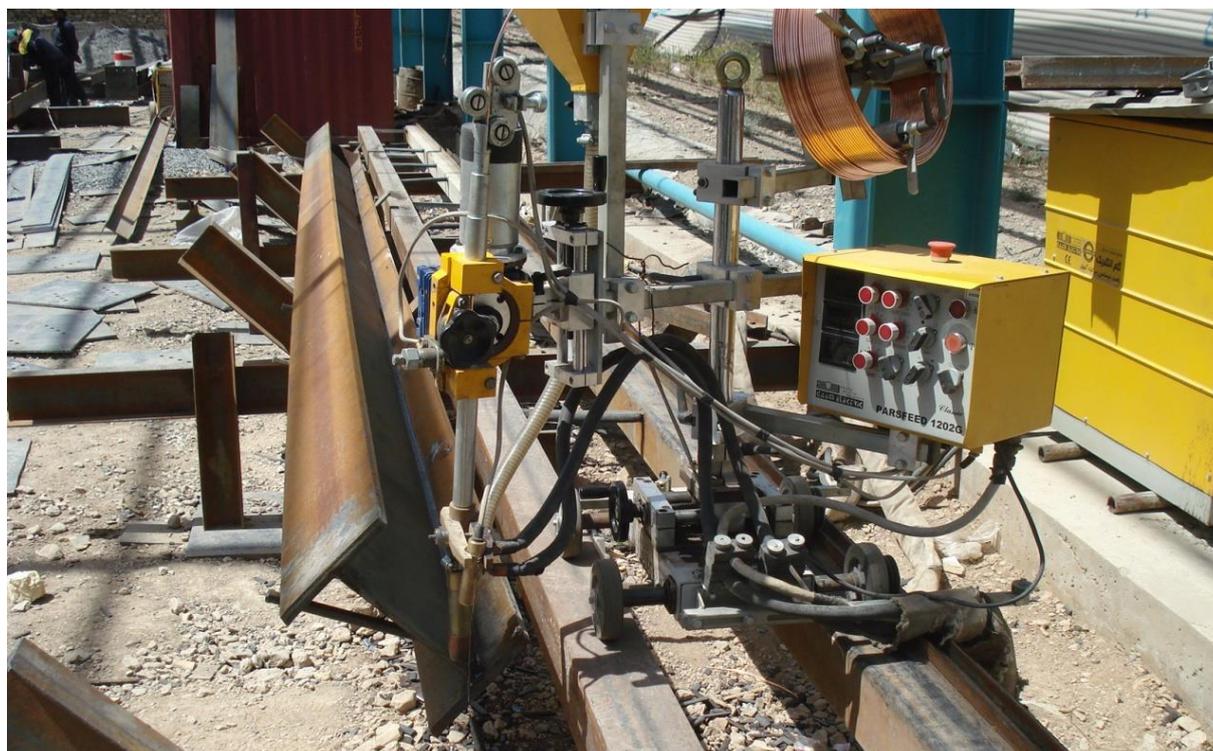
Vorrichtung zum Unterpulverschweißen
